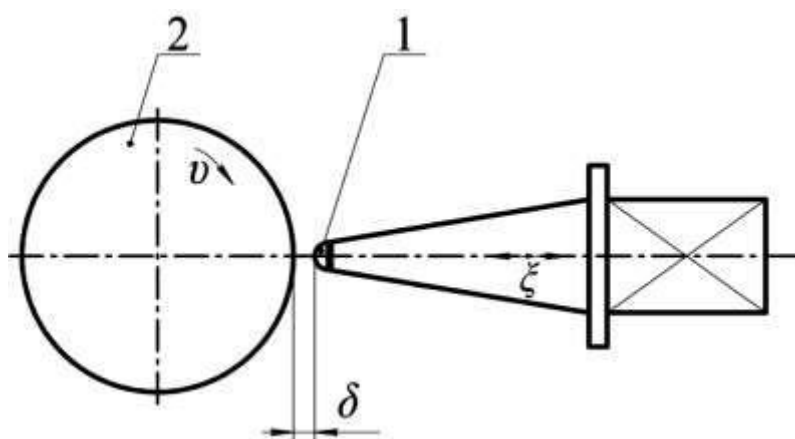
Схема ППД з ультразвуком: 1 – інструмент; 2 – деталь
